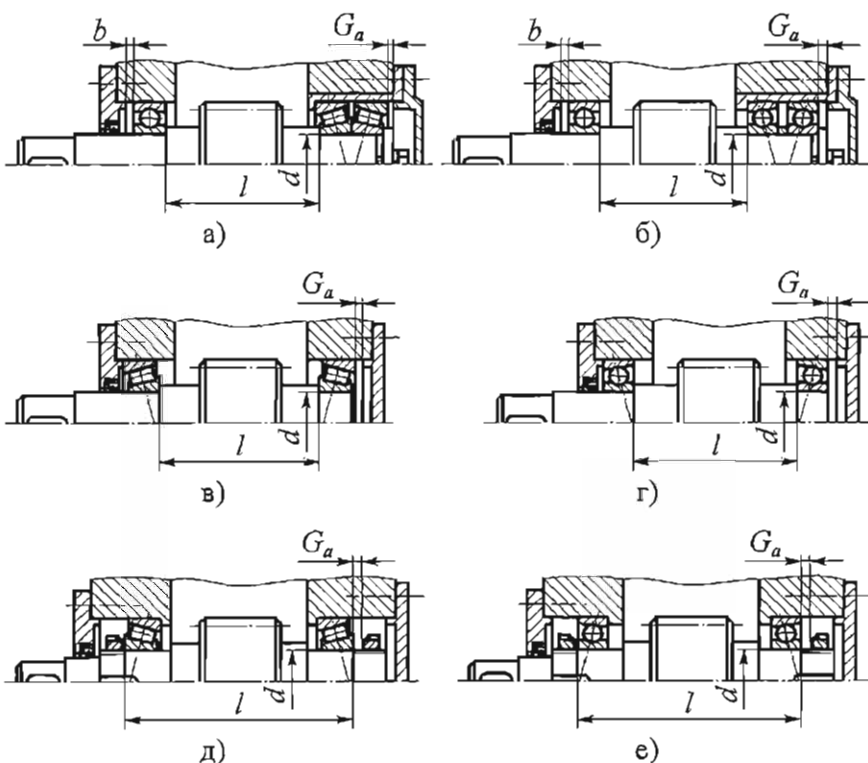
Конструктивные схемы установки подшипников качения в опорах валов:
